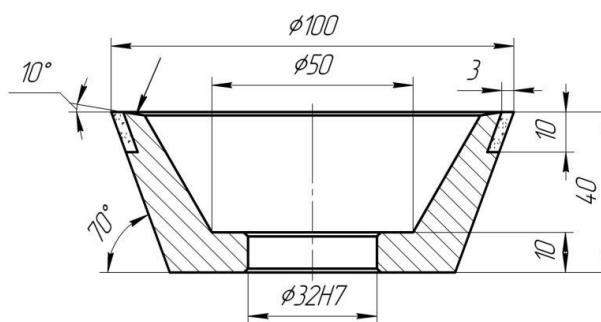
Чертёж круга формы 11V9 100×3×10 с корпусом из композита
